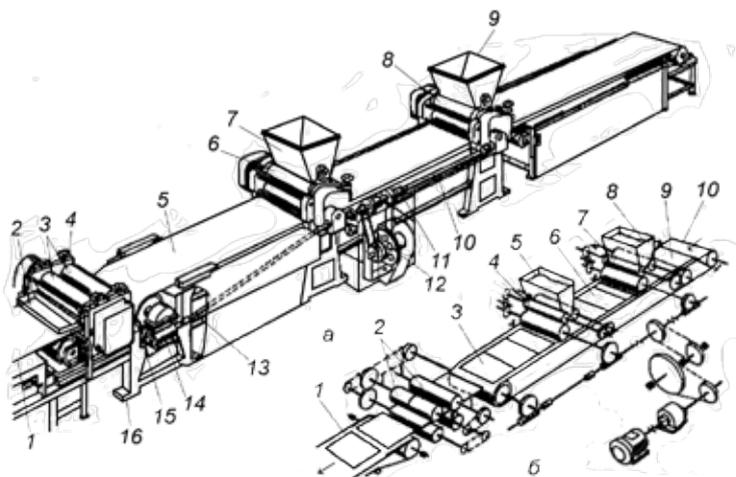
Машина для нанесения начинки на вафельные листы с двумя валковыми механизмами: а — устройство; б — схема образования пласта
